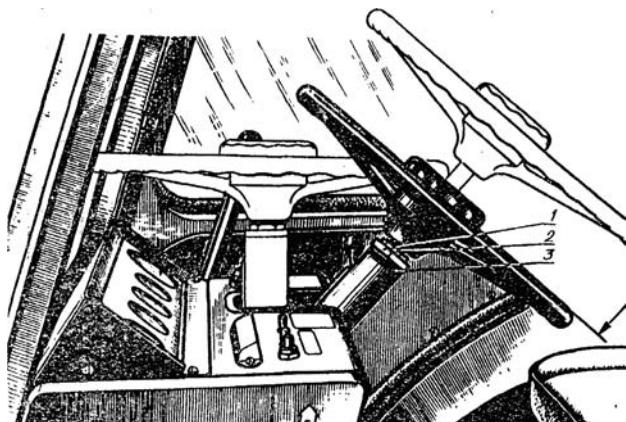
Регулировка рулевой колонки: 1 — гайка; 2 — контргайка; 3 — втулка.
